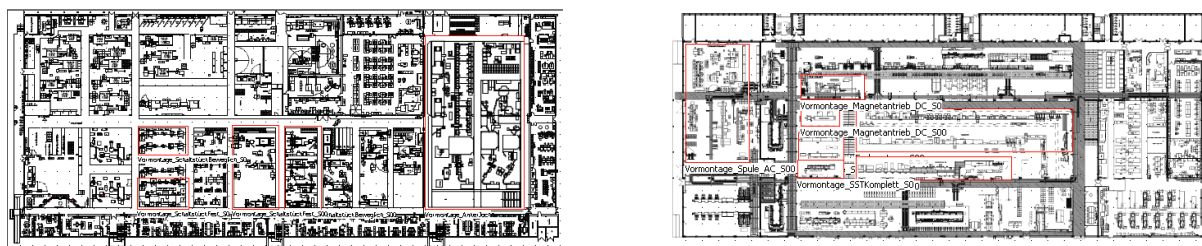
Modellaufbau; Ebene Halle 1 und Halle 4 (eigene Darstellung)
